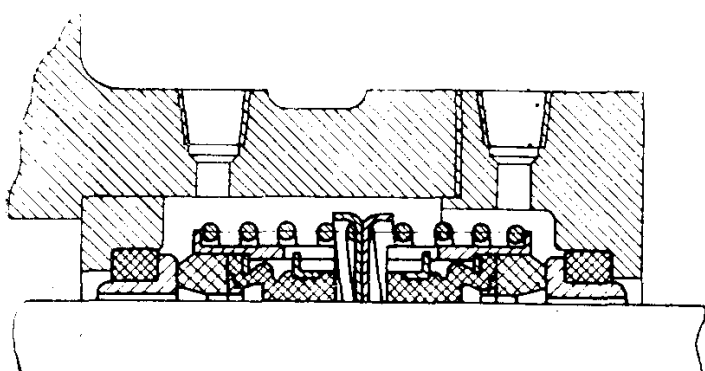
Etanșare mecanică, echilibrată, cu inel fix.
